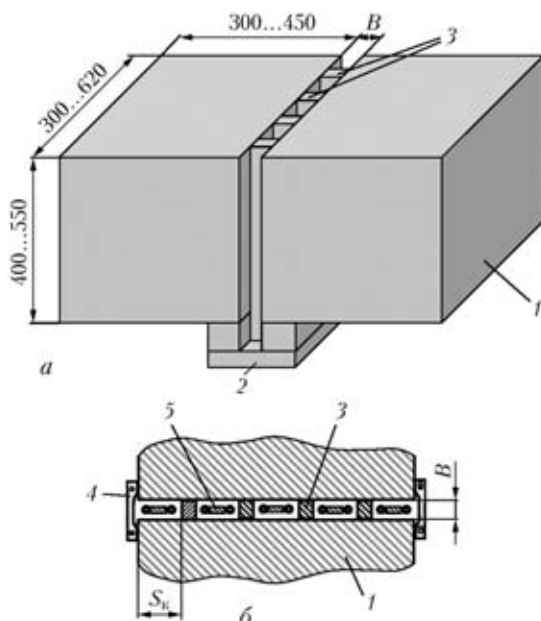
Схема сборки (а) и МЭШС (б) опытных образцов с продольной установкой плавящихся мундштуков: 1 — свариваемые детали; 2 — входной карман; 3 — формирующие пластины-проставки; 4 — водоохлаждаемая накладка; 5 — плавящийся мундштук; В — ширина сварочного зазора; S_k — толщина металла колодца
